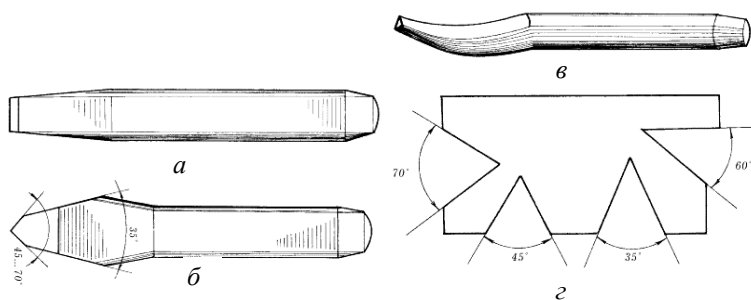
Рубящий инструмент: а) зубило; б) крейцмейсель; в) канавочники; з) шаблон для контроля заточки
